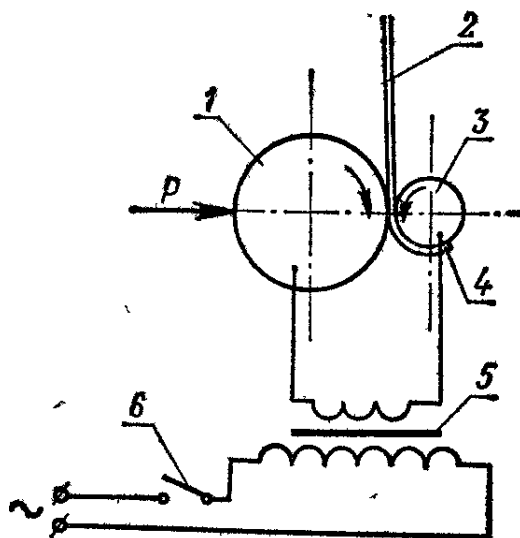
Схема електроконтактного наплавлення: P – притискне зусилля; 1 – притискний ролик; 2 – дріт чи стрічка для присадки; 3 – деталь для наплавлення; 4 – наплавлений шар; 5 – трансформатор; 6 – переривач
